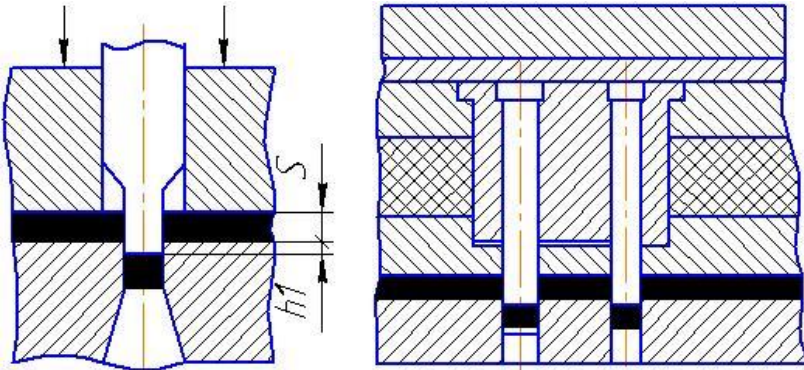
Конструкції пуансонів з малою довжиною робочої частини для обробки товстостісного металу
